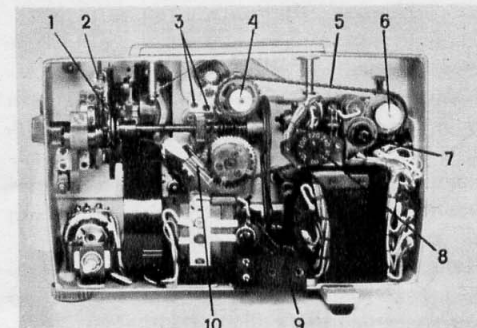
Вид со снятой задней крышкой: 1 — фетровый сальник для смазки кулачков рейфера; 2 — гайка с контргайкой для регулирования усилия прижима рейферной рамки к кулачку; 3 — винты крепления кронштейна сматывателя к корпусу; 4 — гайка с контргайкой для регулирования усилия натяжения фильма при перематке; 5 — цепь передачи вращения на фрикционные; 6 — гайка с контргайкой для регулирования натяжения фильма наматывателем; 7 — предохранитель; 8 — переключатель напряжения; 9 — пассив для передачи вращения от электродвигателя к горизонтальному валу; 10 — контактная группа.
